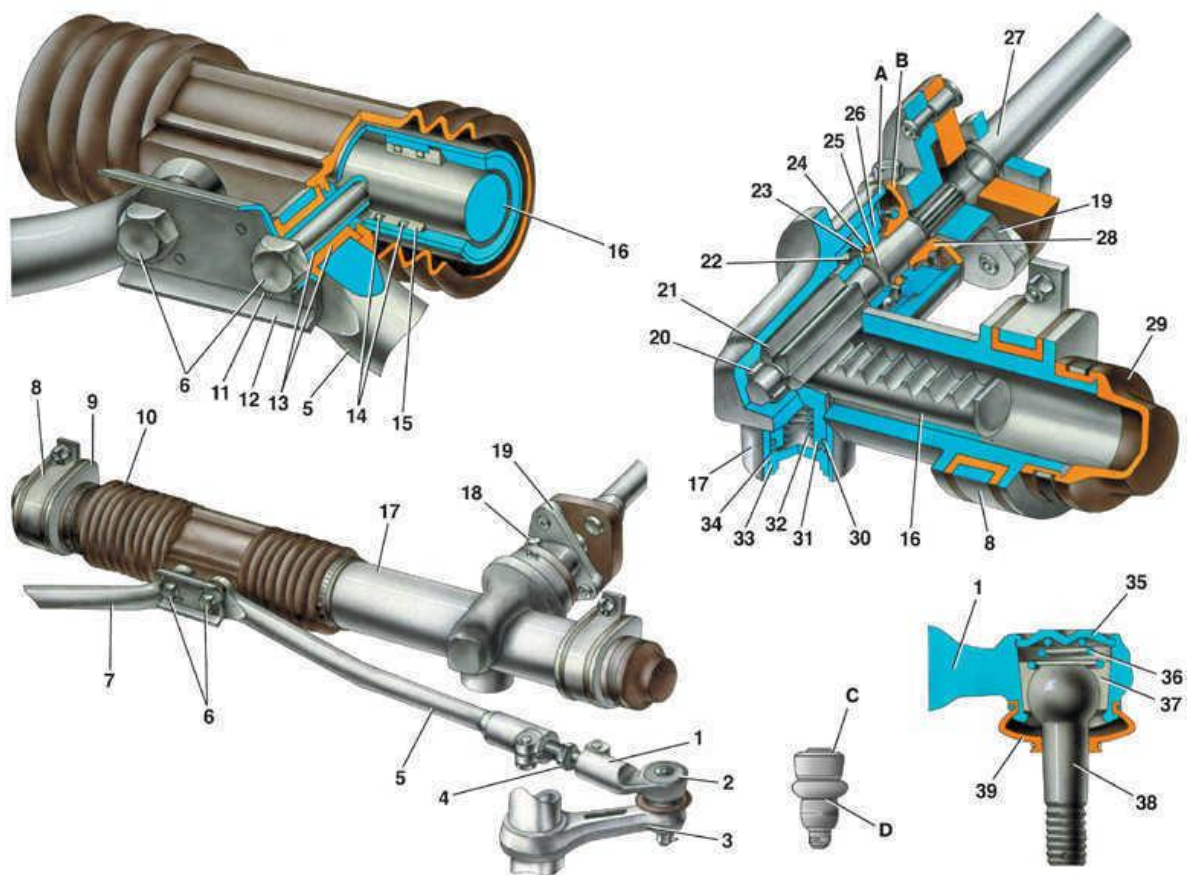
Боковое расположение шестерни при креплении боковых тяг к середине зубчатой рейки
